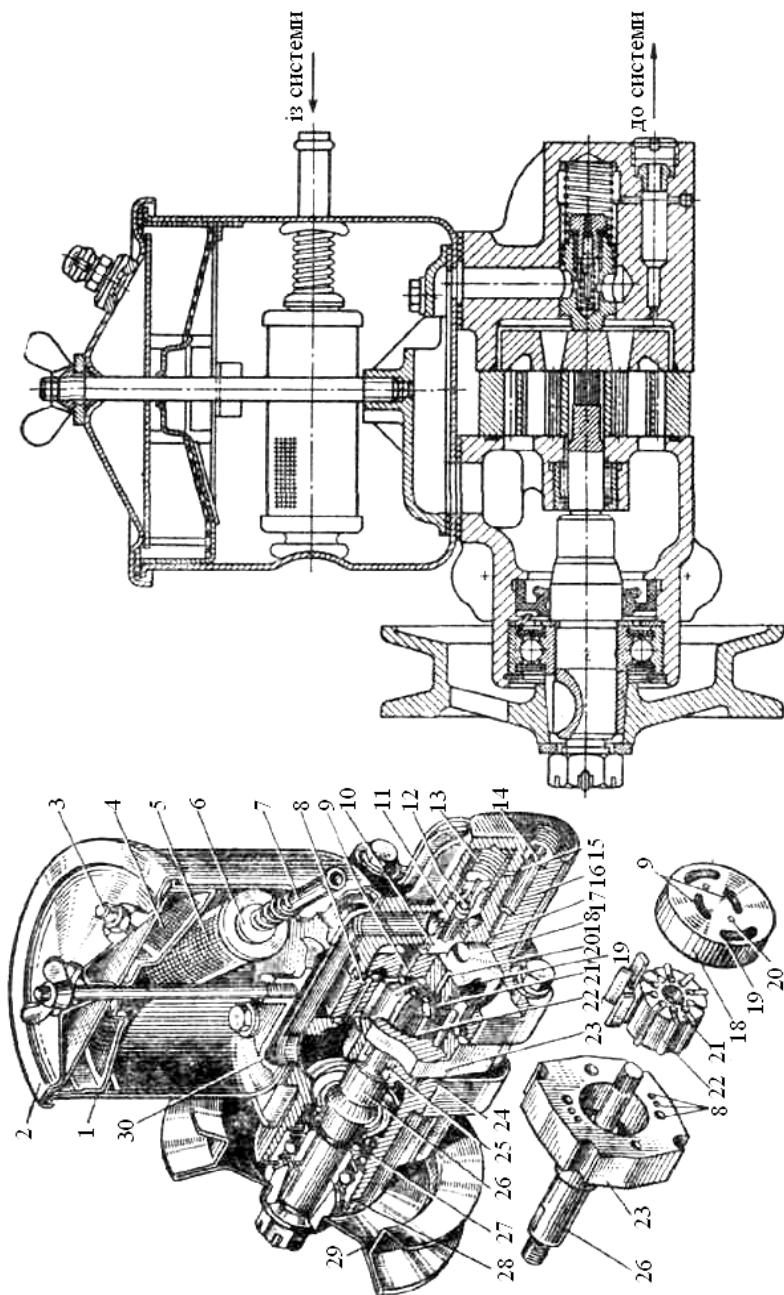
Гідралічний шибєрний насос гідроїдсилювача рульового керування
